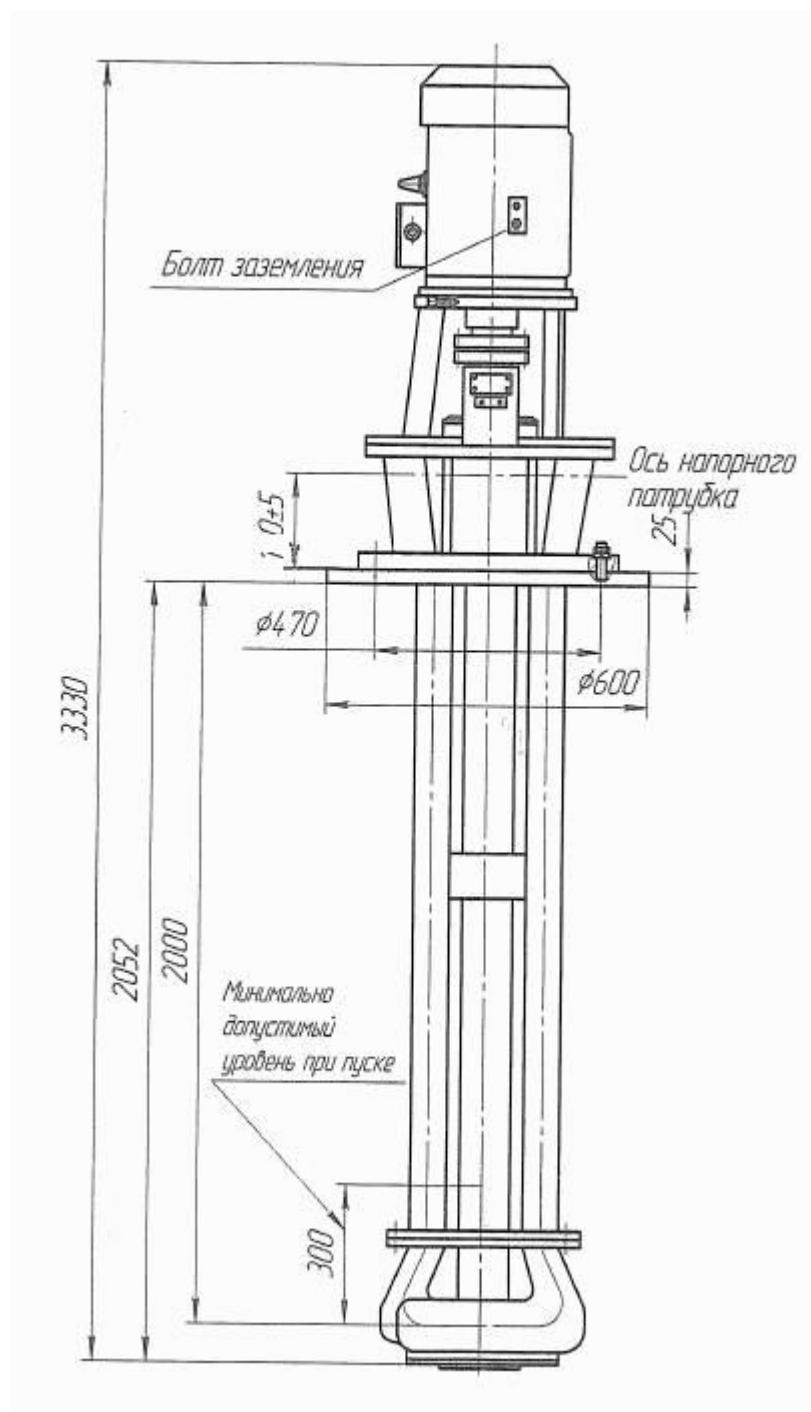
Габаритный чертеж насоса дренажного бака
